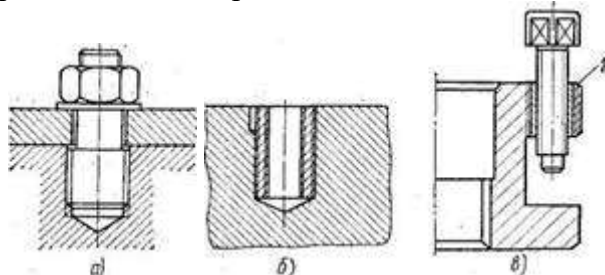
Схемы ремонта резьбовых соединений с помощью установки:
